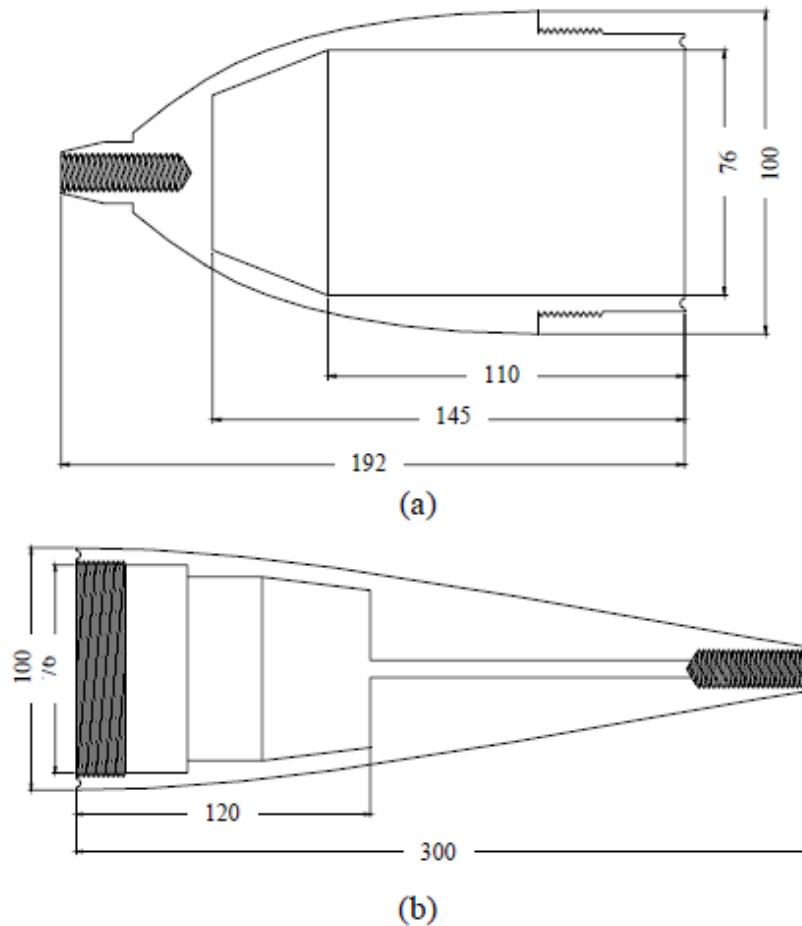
Desenhos para a usinagem das partes do penetrômetro, dimensões em milímetros. (a) Desenho do nariz; (b) Desenho da cauda.
